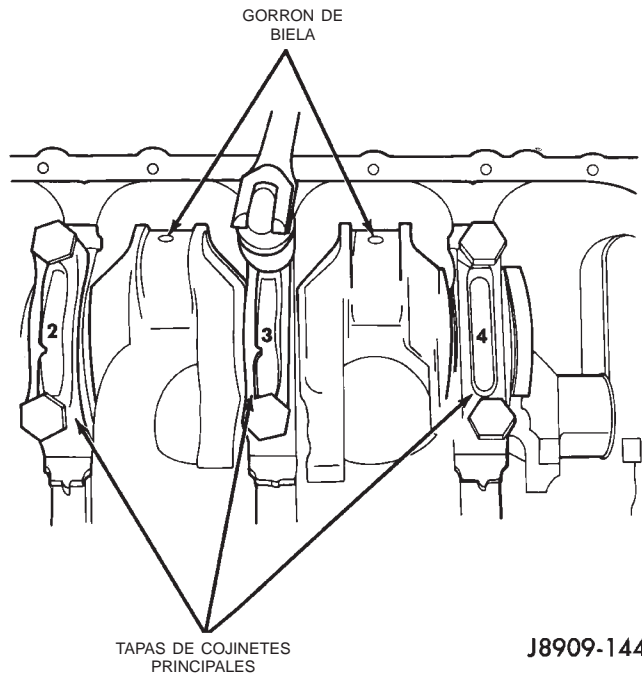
Desmontaje de tapas de cojinetes principales y encastres inferiores
